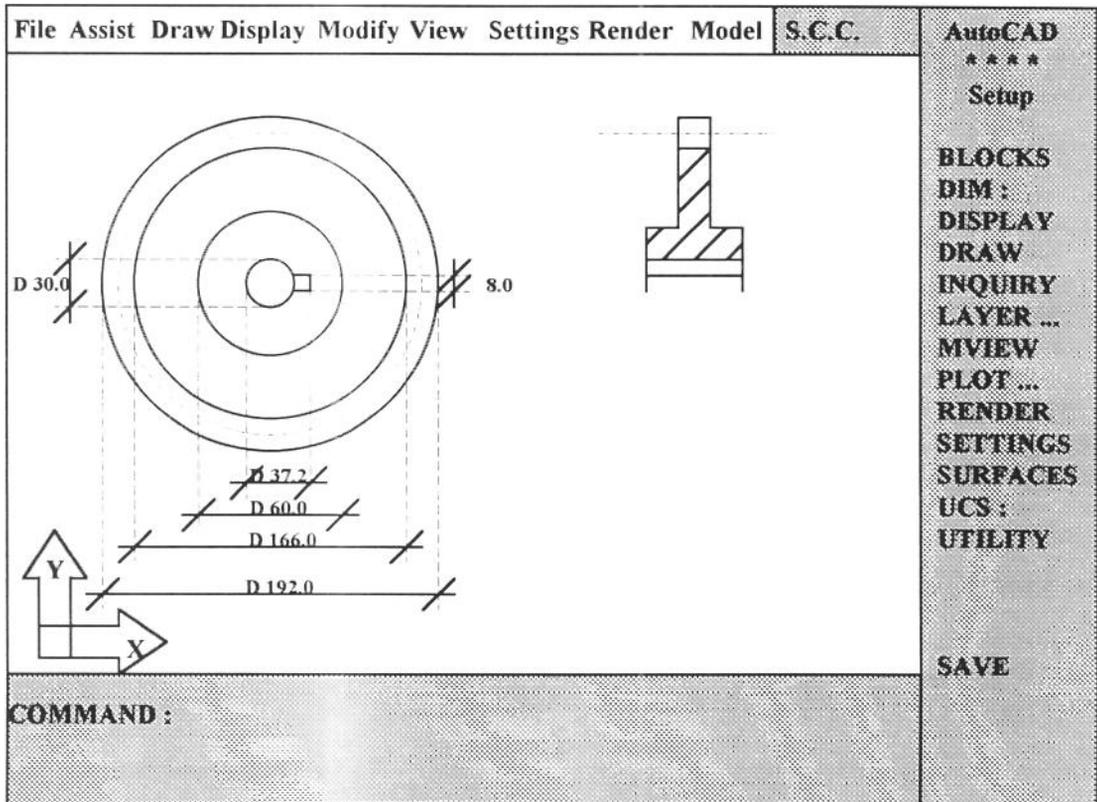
Construção do Corte Transversal - Parte Superior
